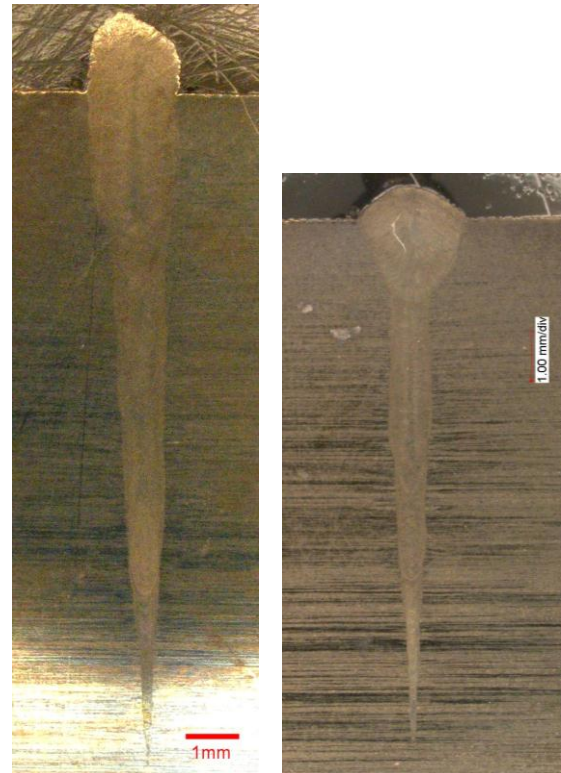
Schweißergebnisse mit 3 kW Monomode Faserlaser, links: Blindschweißung mit Scanner $f = 500$ mm und $v = 0,5$ m/min: 13 mm Einschweißtiefe in Edelstahl 1.4301.
